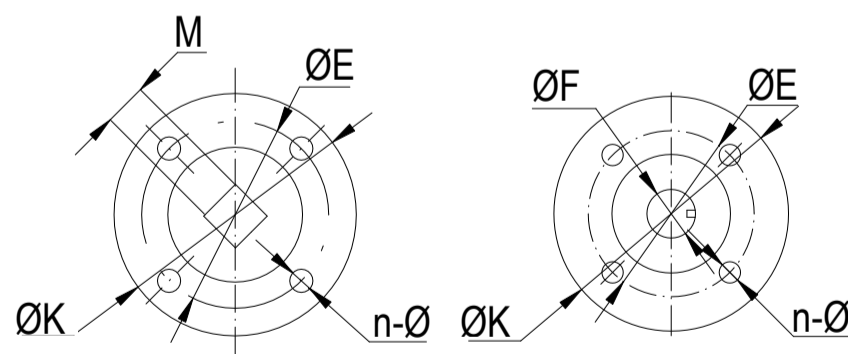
Wymiary podstawowe, na czarno zaznaczono otwory gwintowane | Basic dimensions, marked in black holes mark threaded holes | Размеры основной черной выбран резьбовые отверстия
